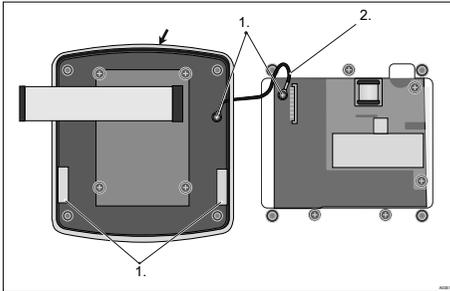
Установка профильного уплотнения на верхней части корпуса регулятора
